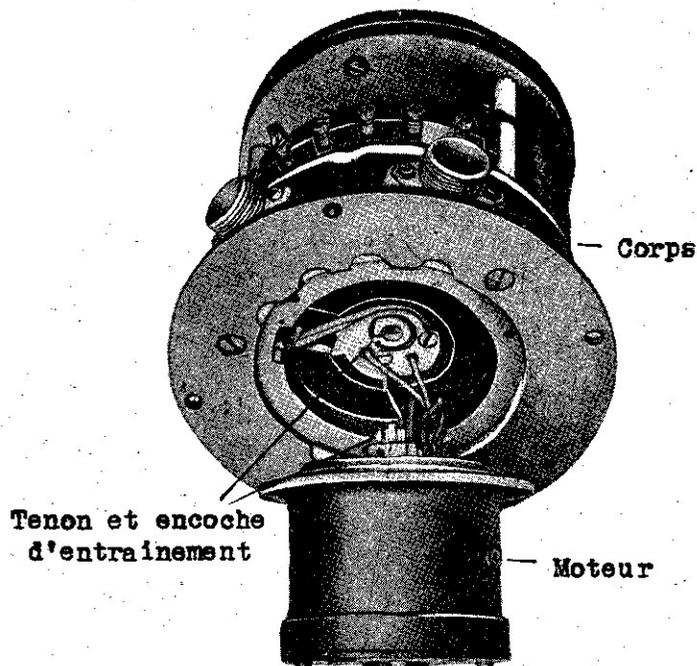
Correcteur de réglage de déclinaison, ensemble moteur.
